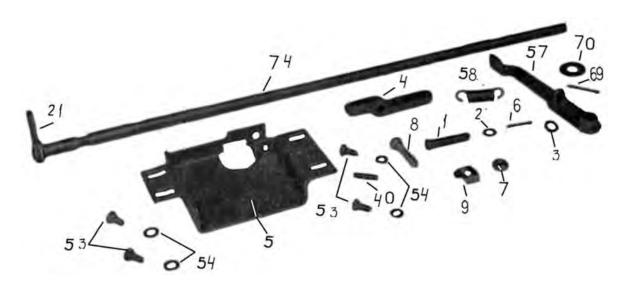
Детали блокирующего устройства: 1, 74 – оси; 2, 54, 70 – шайбы; 3, 58 – пружины; 4, 21, 57 – рычаги; 5 – кожух в сборе; 6, 69 – шплинты; 7 – гайка; 8 – регулятор; 9 – скоба; 40 – штифт; 53 – болт
